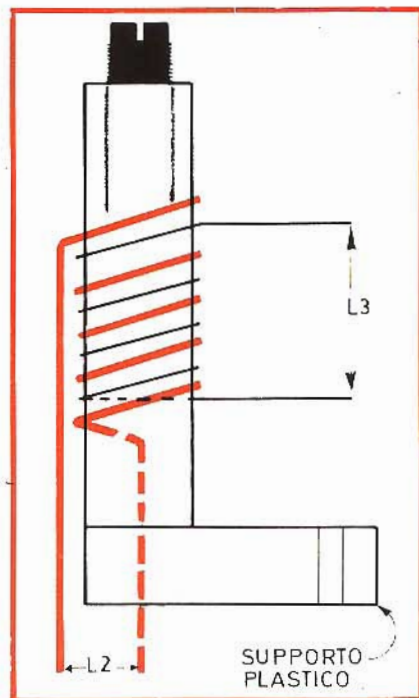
Disegno illustrante la realizzazione della L2-L3.
